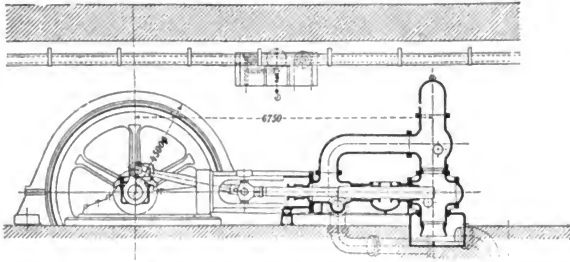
Längsangehender Motor mit Pumpe. Aufriss.
